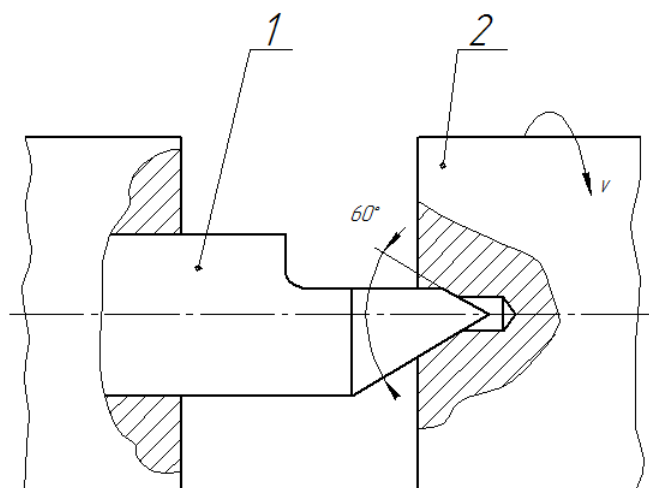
Будова зрізаного центра для обробки торцевих поверхонь деталей: 1 – центр; 2 – деталь
